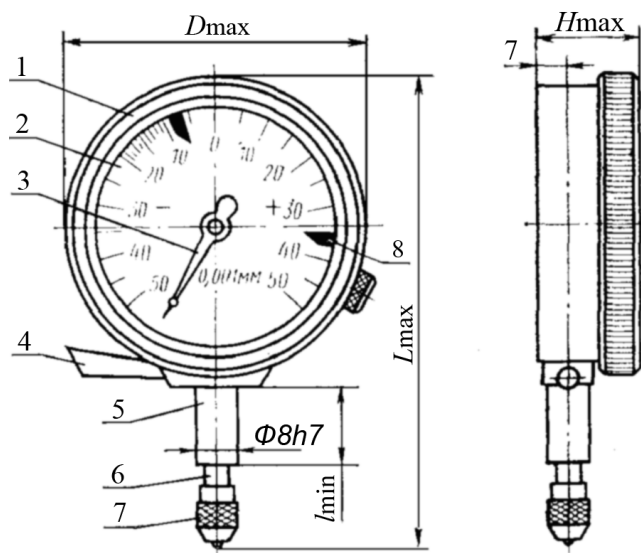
Внешний вид и основные размеры измерительных головок типа ИГ:
